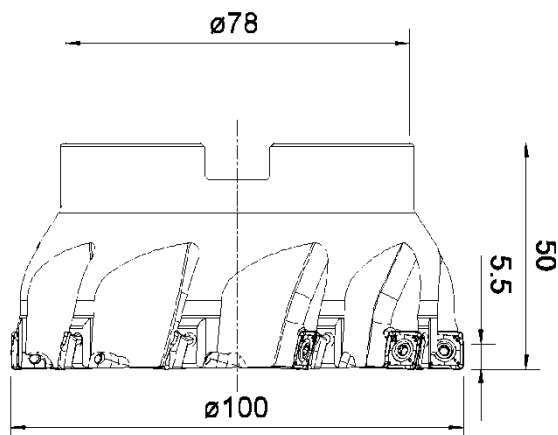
Фреза для обработки прямоугольных уступов 490-100Q32-08Н
